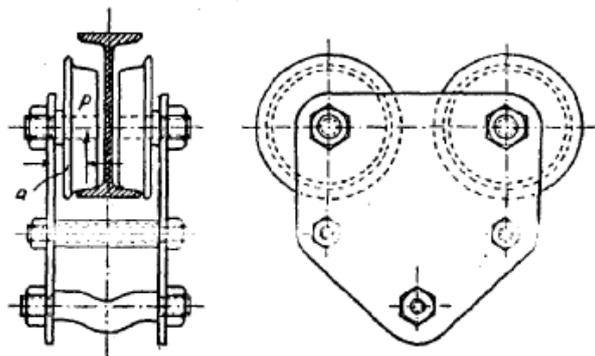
Carro apoyado sobre las alas inferiores de una viga para ponerle un tecele de cadena suspendido.
